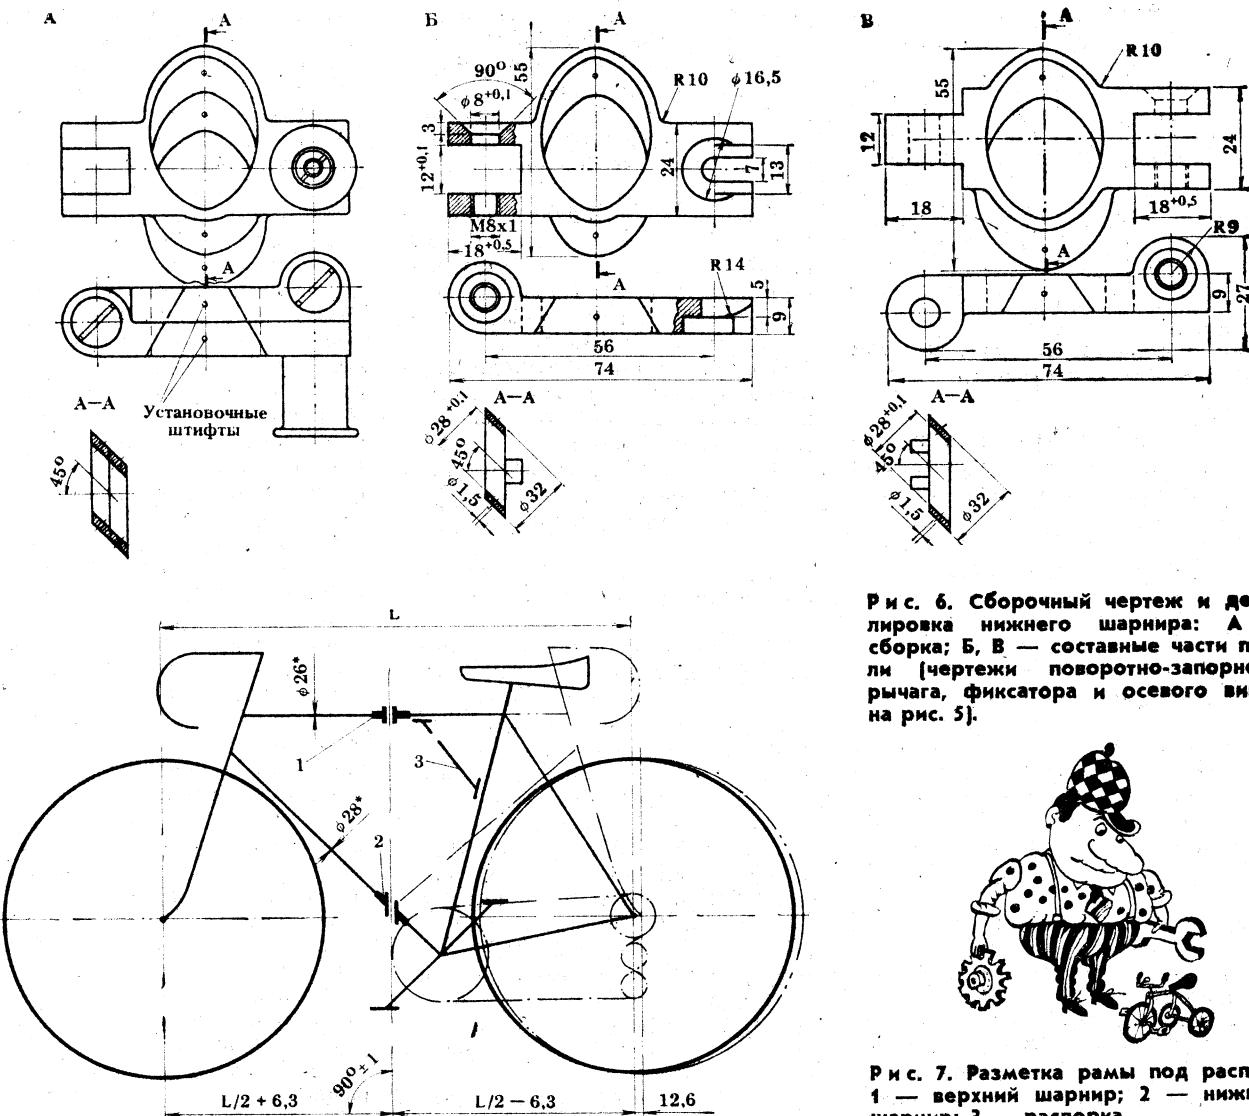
Сборочный чертеж и деталировка нижнего шарнира: А — сборка; Б, В — составные части петли (чертежи поворотно-запорного рычага, фиксатора и осевого винта на рис. 5).
